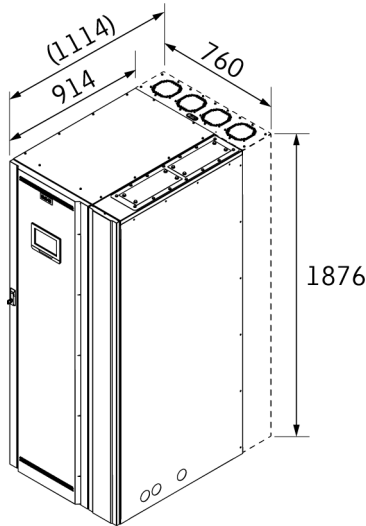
Dimensions d'UPS 93PM 160-250 kVA
